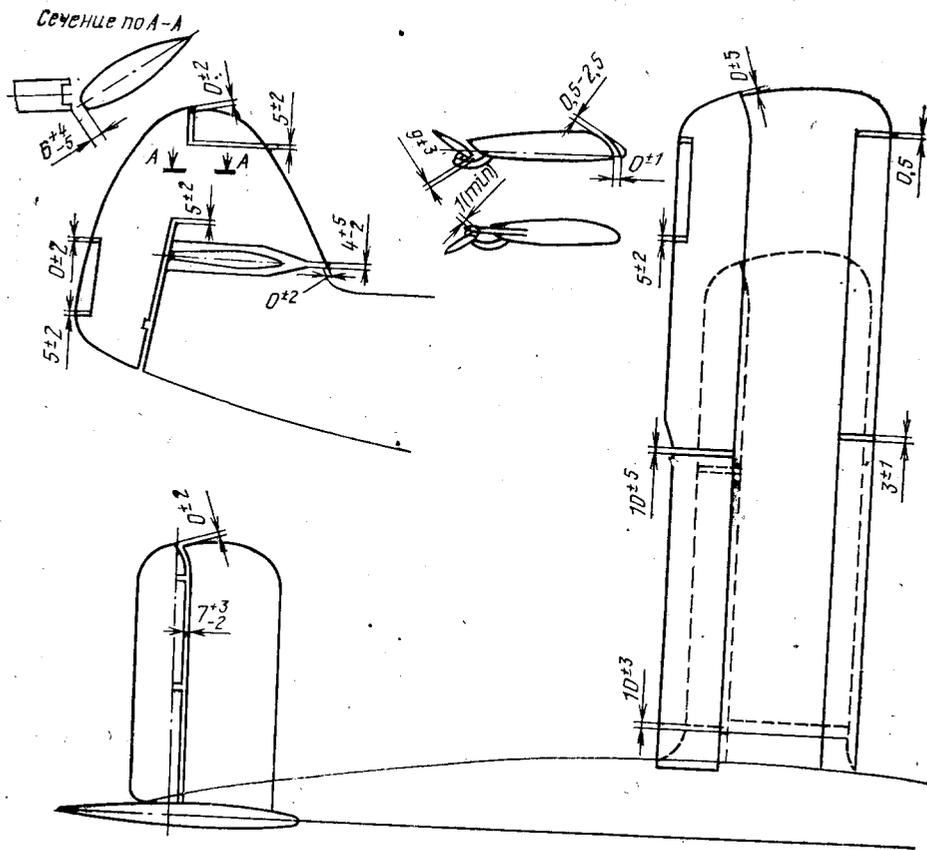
Схема зазоров в агрегатах крыла и оперения
